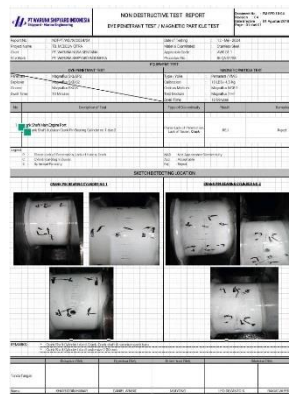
Uji *magnetic particle inspection (MPI)* dan kondisi keretakan *crankshaft* dudukan *crank pin bearing
